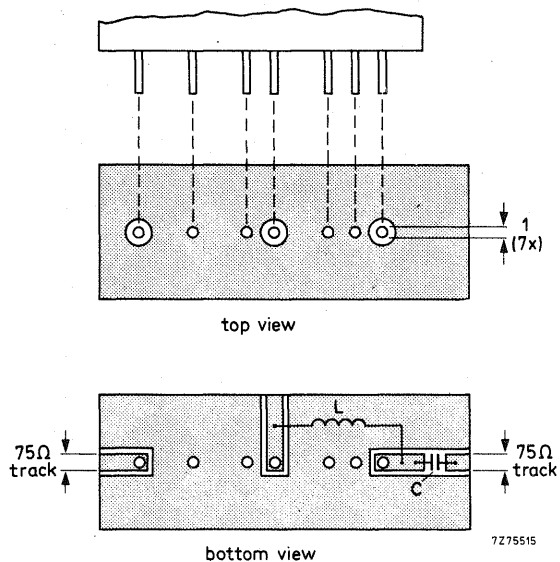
Sistema di montaggio consigliato dei moduli OM336 e OM339 sulla piastrina di circuito stampato
